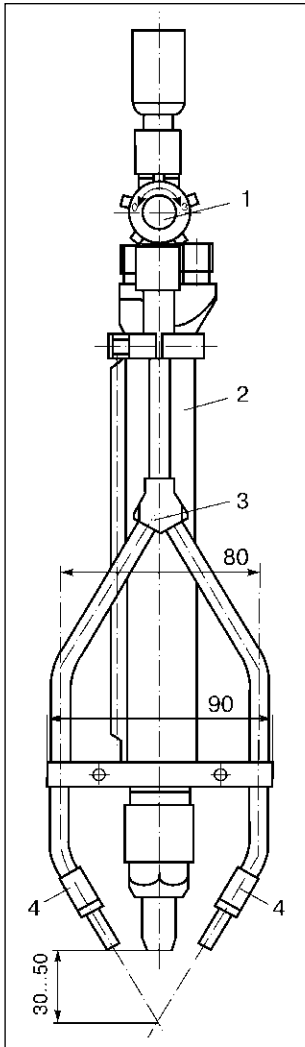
Установка машинного резака: 1 — вентиль для флюса; 2 — резак «Эффект-М»; 3 — трубка подачи флюса; 4 — сопла для флюса
